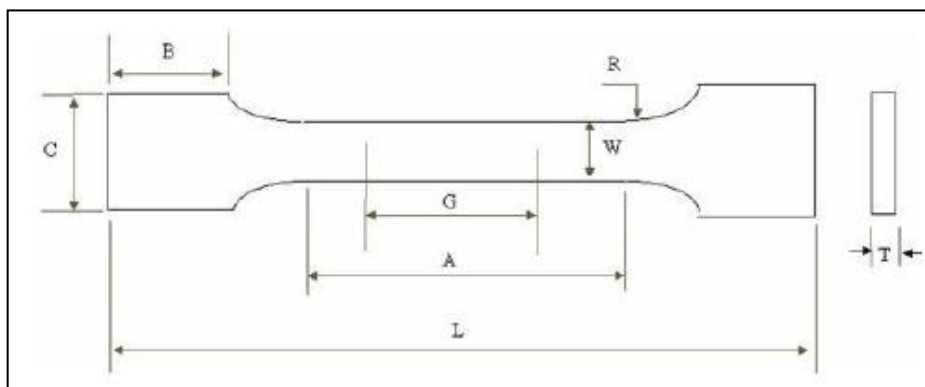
Amostra para ensaio de tração ASTM<sup>[40]</sup>
